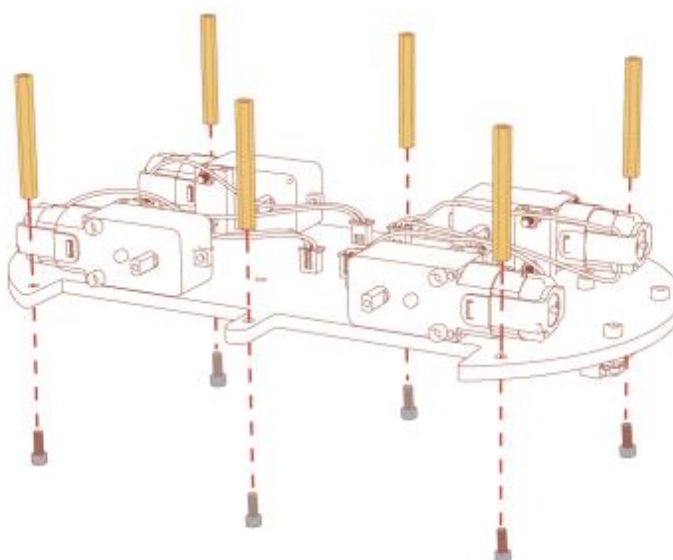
Підготовка до об'єднання верхньої та нижньої платформ
